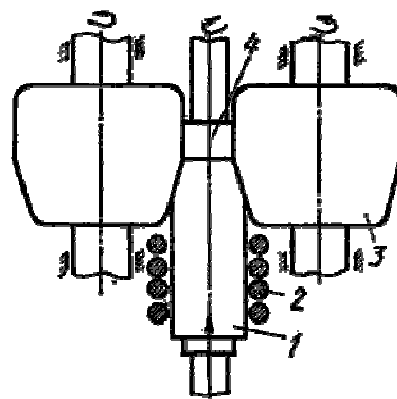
Схема прокатки шестерни с осевой подачей заготовки
